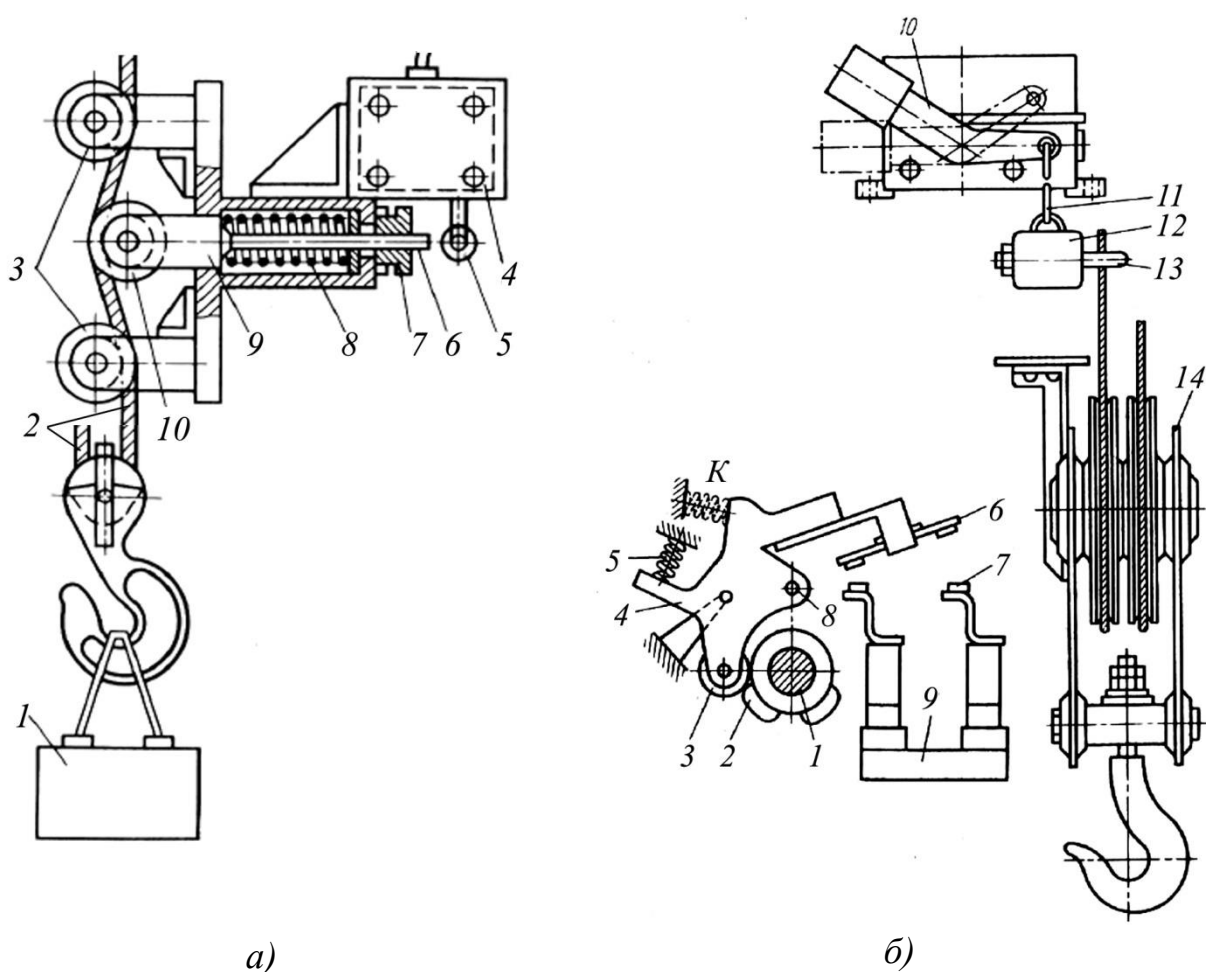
Механический ОГП с упругим элементом в виде цилиндрической пружины (*а*); рычажный конечный выключатель (*б*)
